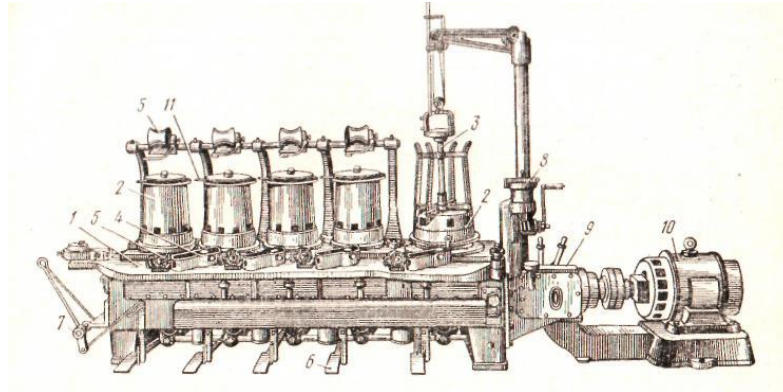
Машина 5/350 багатократного волочиння: 1 - станина; 2 - барабан; 3 - знімач; 4 - мильниця з волокодержателем; 5 - направляючі ролики; 6 - педаль включення і виключення; 7 - вимикач при заплутуванні мотка; 8 - знімний пристрій; 9 - коробка швидкостей; 10 - двигун; 11 - повідкове пристрій
